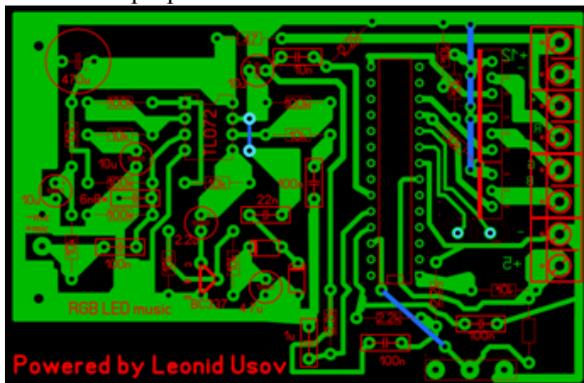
Разводка печатной платы в CAD Sprint Layout 6.
